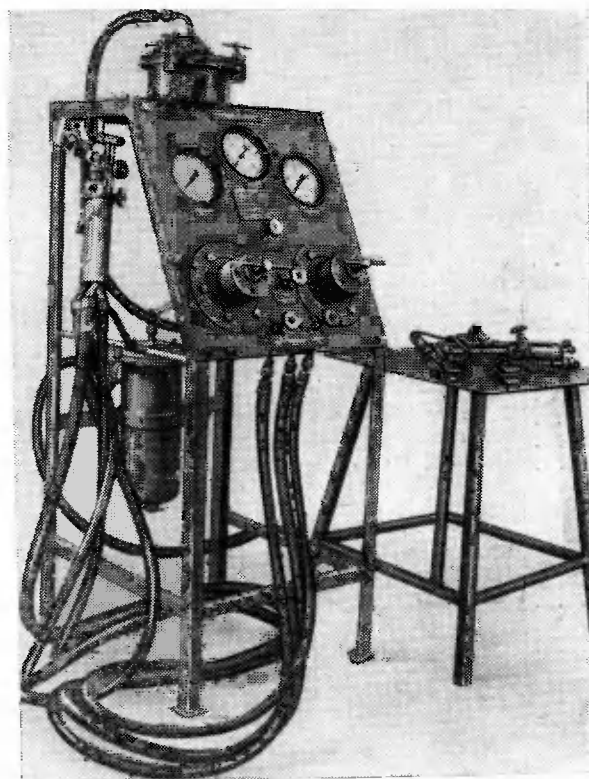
Установка УПН-4 для газопламенного напыления покрытий из пластмасс
